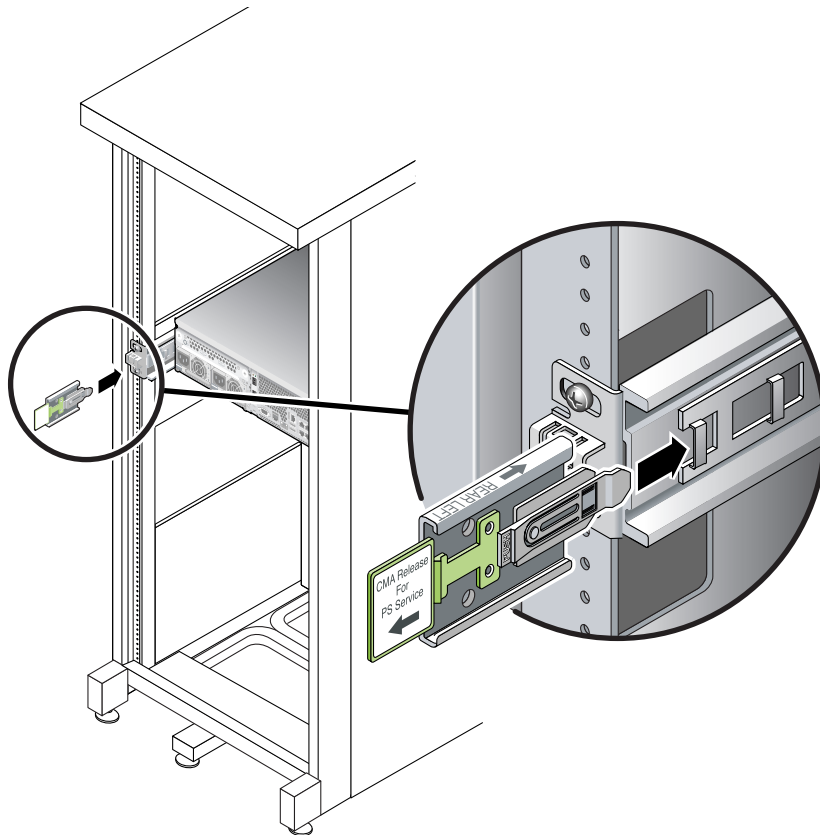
Inserción de la extensión de la guía CMA en la parte posterior de la guía deslizante de la izquierda
